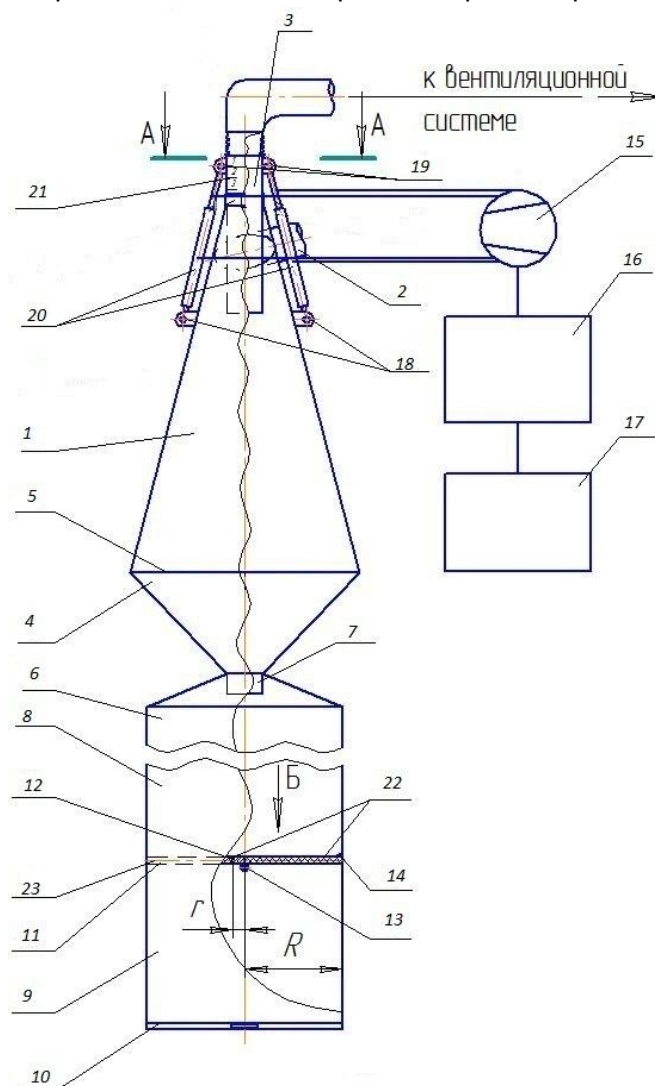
Пылеулавливатель: 1 — верхний конус циклона; 2 — входной патрубок; 3 — выхлопной патрубок; 4 — нижний конус циклона; 5 — основания конусов; 6 — пылесборник; 7 — патрубок; 8 — верхний отсек пылесборника; 9 — нижний отсек пылесборника; 10 — задвижка; 11 — перегородка; 12 — полукруглые люки; 13 — противовесы; 14 — ось, относительно которой вращается перегородка; 15 — нагнетательное устройство; 16 — блок управления; 17 — источник питания; 18 — кольцевой упор; 19 — проушины; 20 — основания пневмоцилиндров; 21 — выдвигаемые штоки пневмоцилиндров; 22 — шкала с делениями; 23 — кольцевой упор
